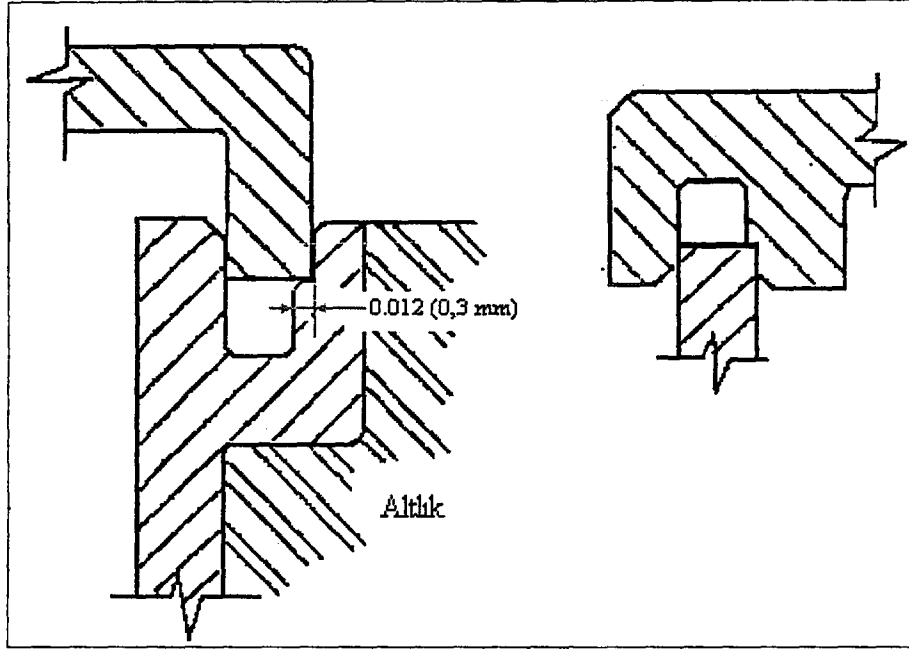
Çeşitli kesme kaynak tasarım şekilleri
